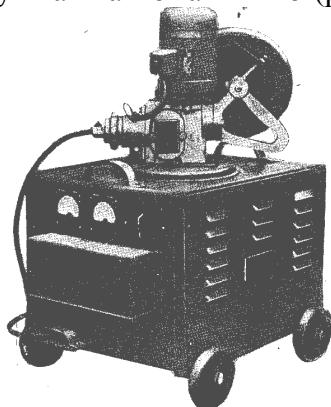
Напівавтомат для дугового зварювання під флюсом типу ПШ-5 (1948)
